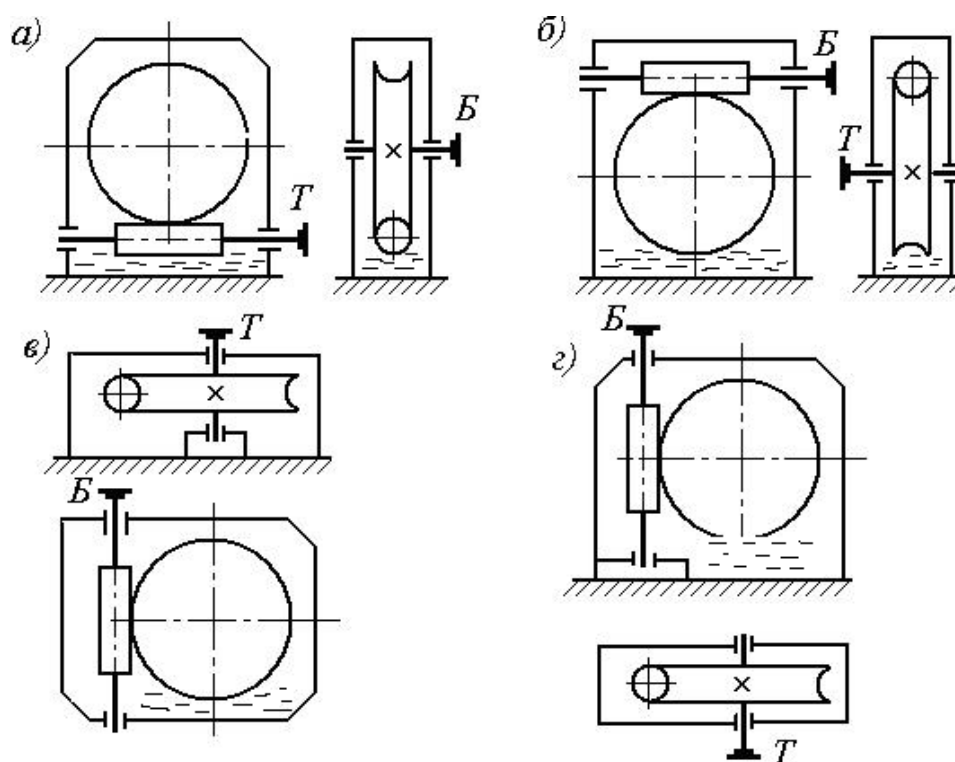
Схемы смазывания одноступенчатых червячных редукторов
